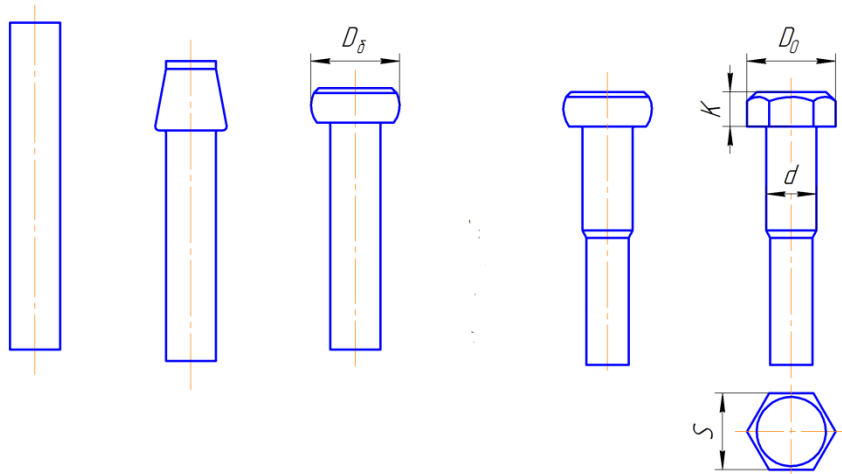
Схема технологического процесса изготовления болтов с обрезкой головки на шестигранник (вариант I)
